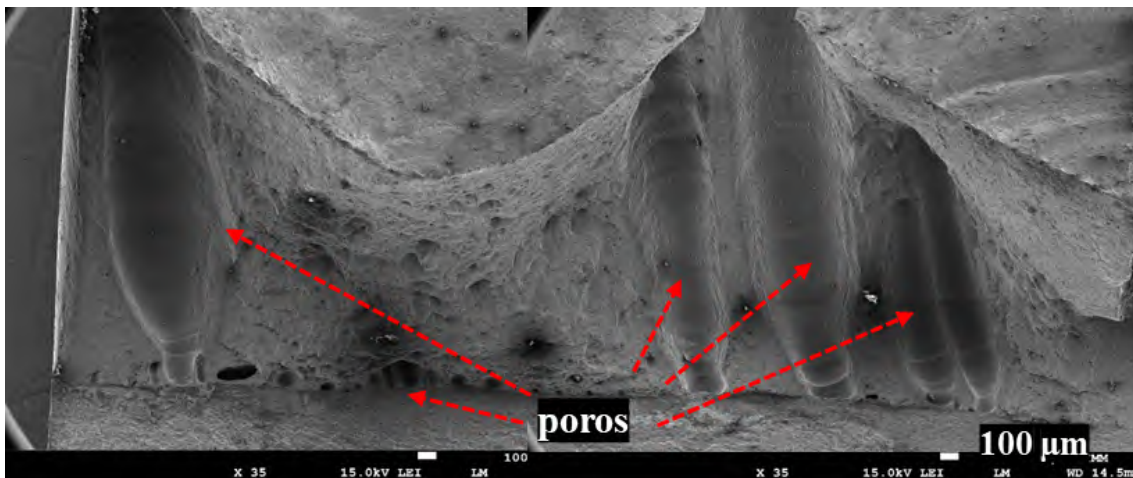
Superficie de fractura de la soldadura S7 con múltiples poros distribuidos a lo largo de la zona fundida.
